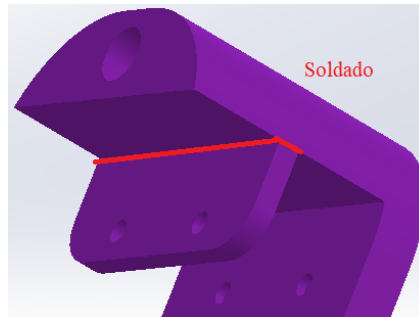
Vista detalle de soldado de pieza N°7 (Fuente 95)
